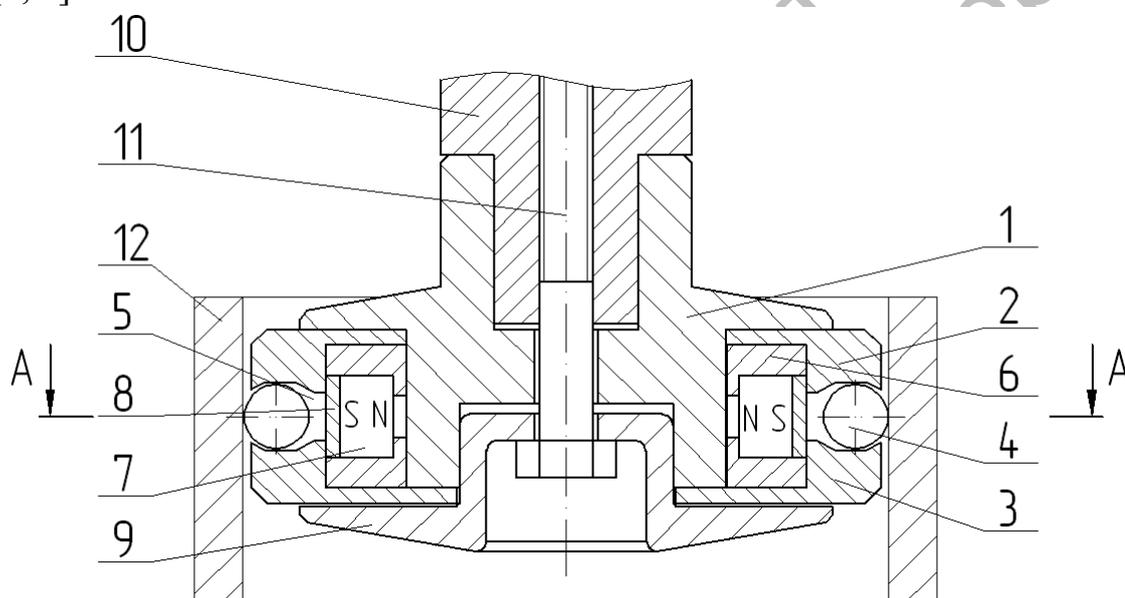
Конструкция магнитно-динамического раскатника для отделочно-упрочняющей обработки поверхности отверстий
